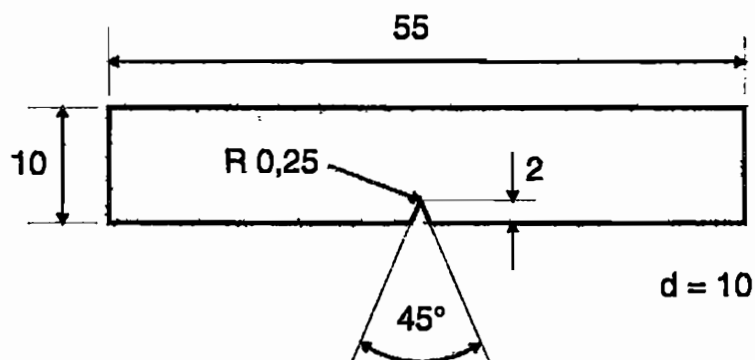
Standard-Charpy-Probe mit V-Kerb nach ASTM E 23 (Charpy Simple-Beam Impact Test Specimen, Type A) [80] bzw. DIN EN 10045-1 [81]
